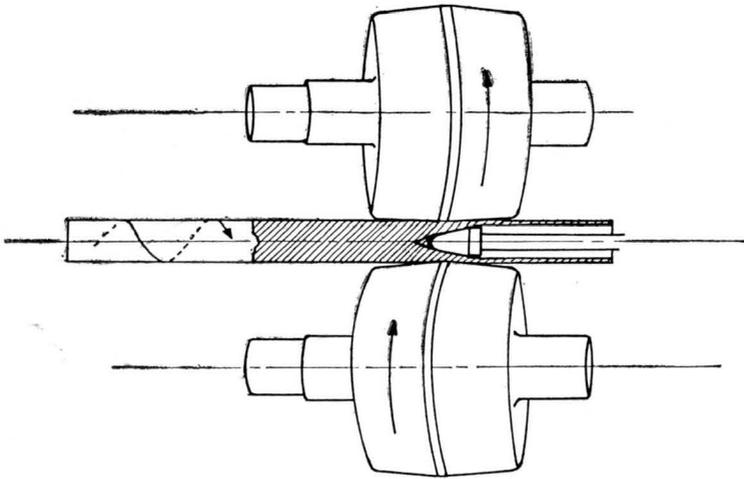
Rolos oblíquos para laminador automático, em forma de tonel.
